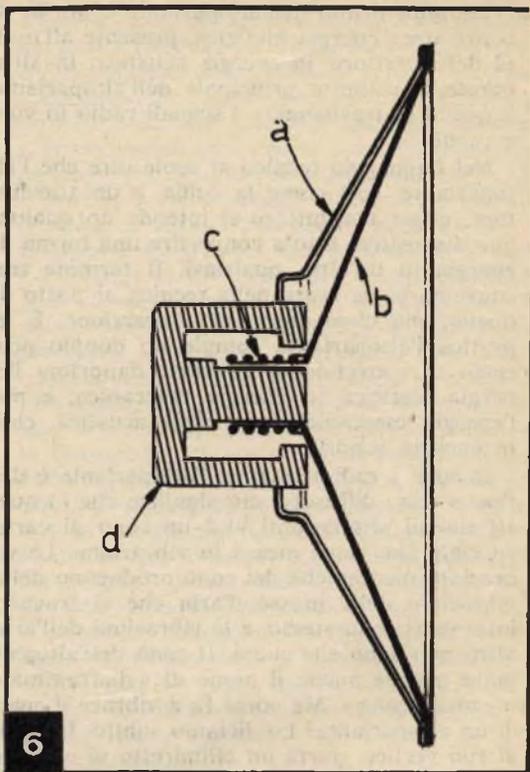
Il disegno riproduce schematicamente un altoparlante magnetico con tutte le sue parti componenti:
